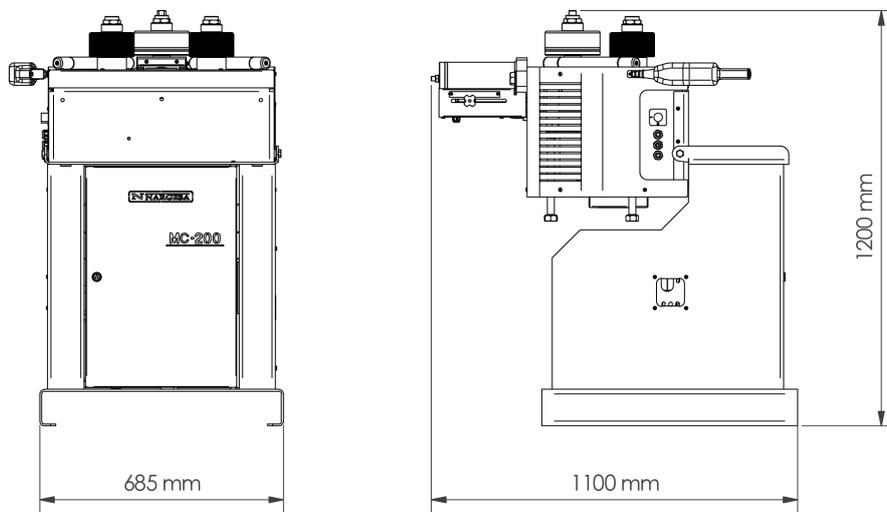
Dimensiones de la máquina con la bancada en posición horizontal
